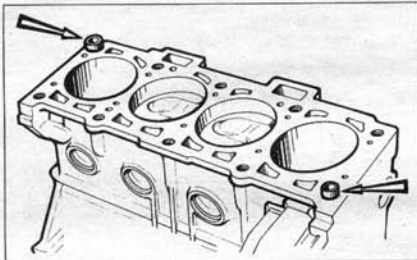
Втулки для центрирования головки на блоке цилиндров
